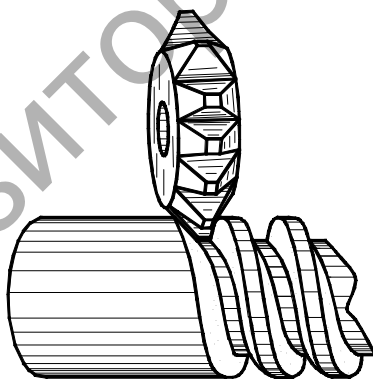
Нарезание витков червяка дисковой фрезой [65]
